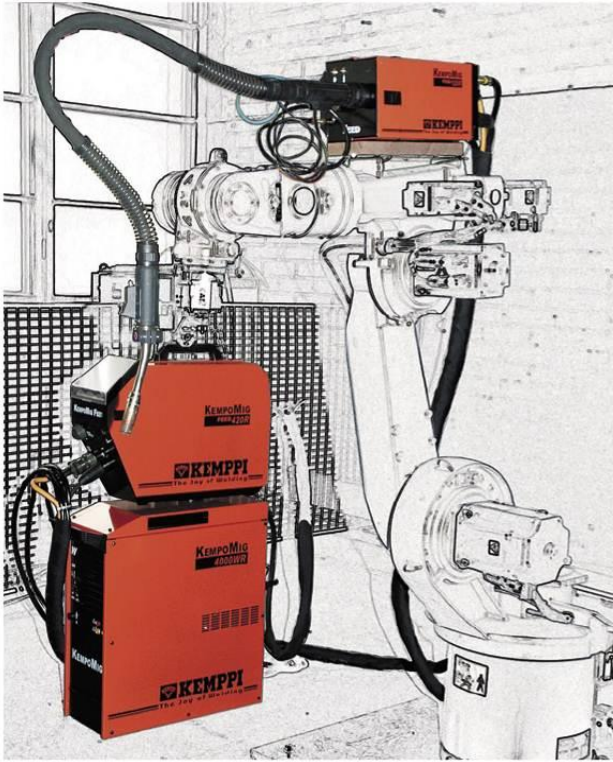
Роботизированный комплекс для сварки на базе установки Kemppi
